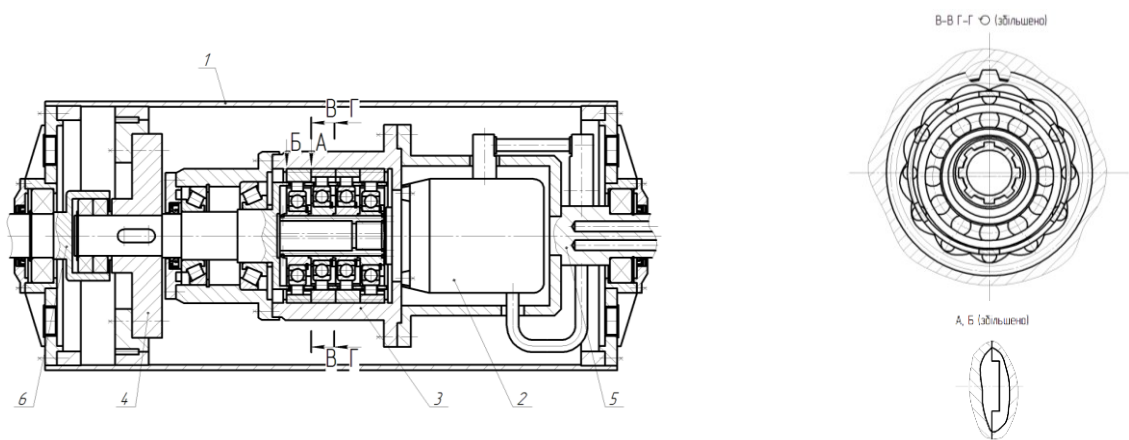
Конструктивна схема вмонтованого гідравлічного привода фрезерного барабана
